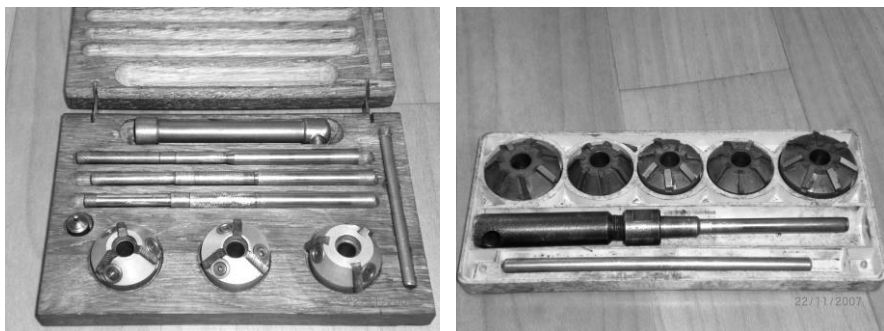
Спеціальні фрези для обробки клапанних гнізд
